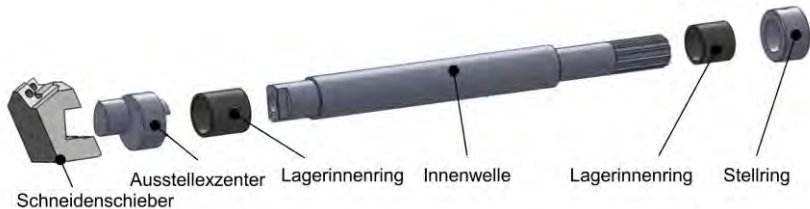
Schneidenhubmechanismus im Werkzeug
